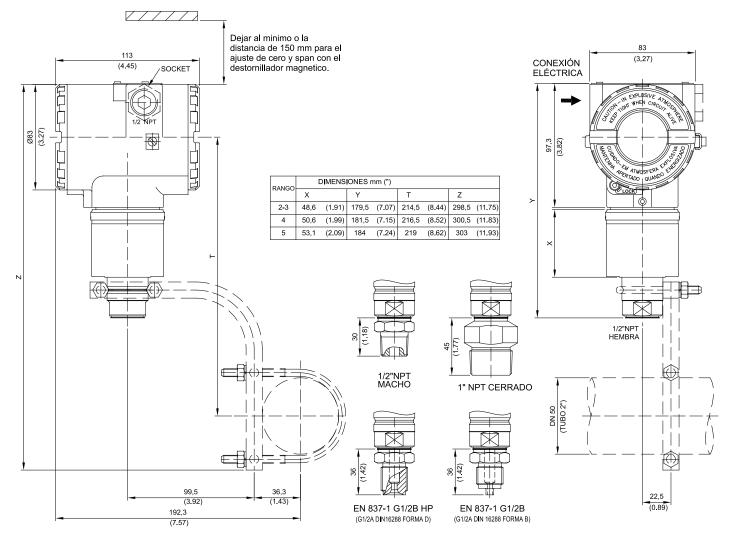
(a) – Diseño Dimensional de Montaje del LD291- Manometrico
